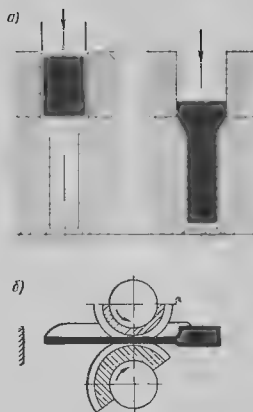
Схема выдавливания лопаток (а) и валцовки на ковочных валцах (б)
